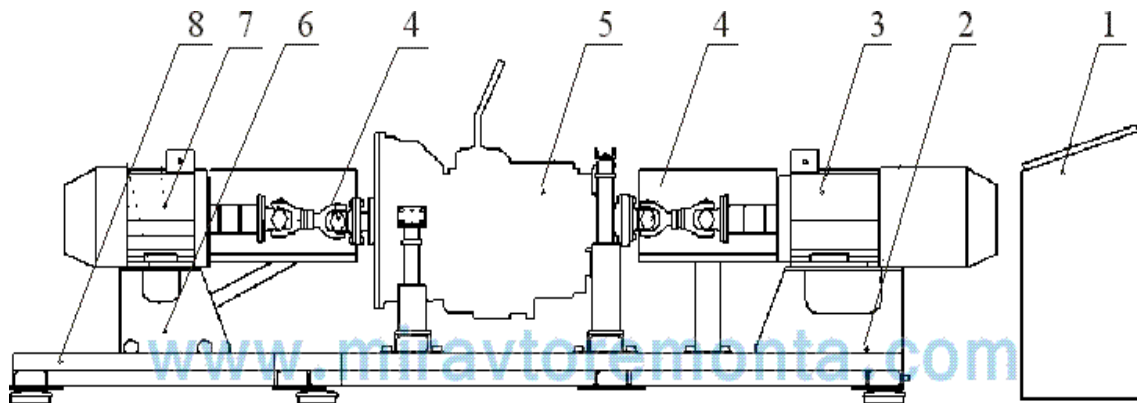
Принципова схема станда для обкатки та випробування коробок передач.
